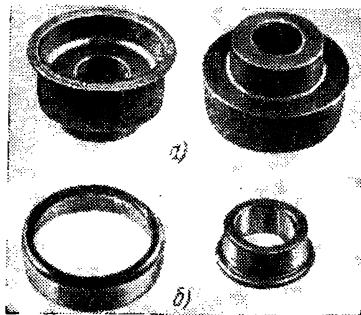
Фото поковок и обработанных деталей подшипниковых колец: а — «башенная» поковка (два кольца); б — кольца после механической обработки
